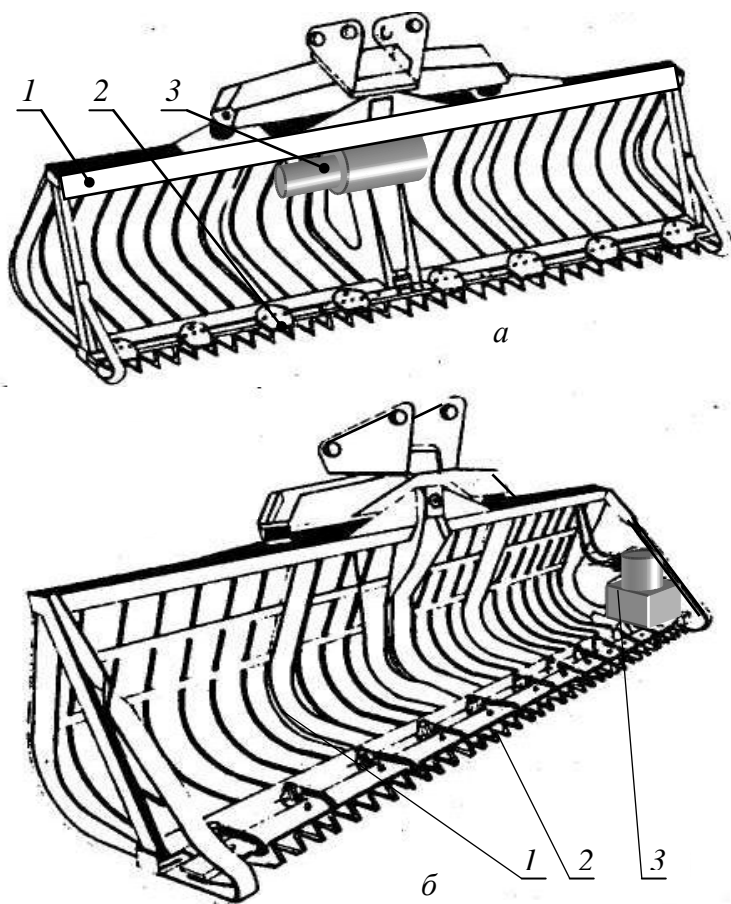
Рабочий орган ковша-косилки: а – с центральным расположением привода; б – с боковым.
